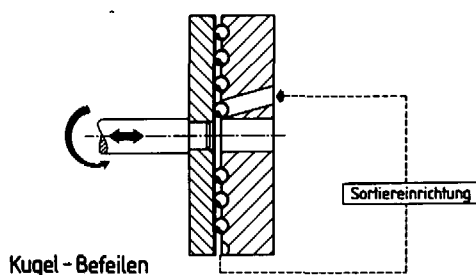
Prinzipskizze einer Kugel-Befeilmachine
